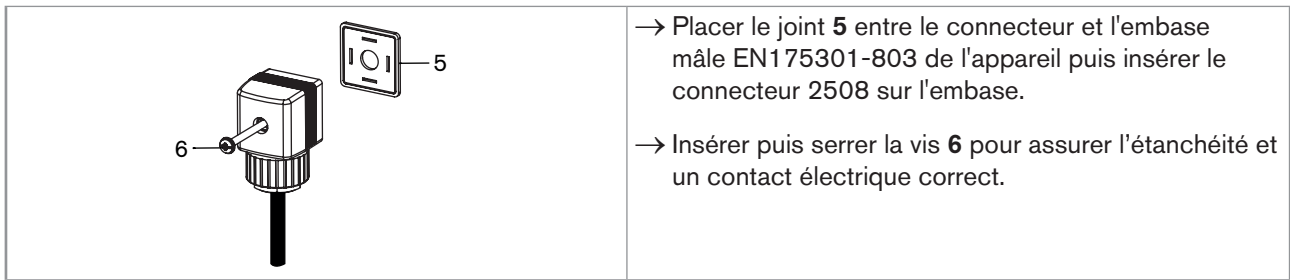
Assemblage du connecteur femelle type 2508 (fourni)
